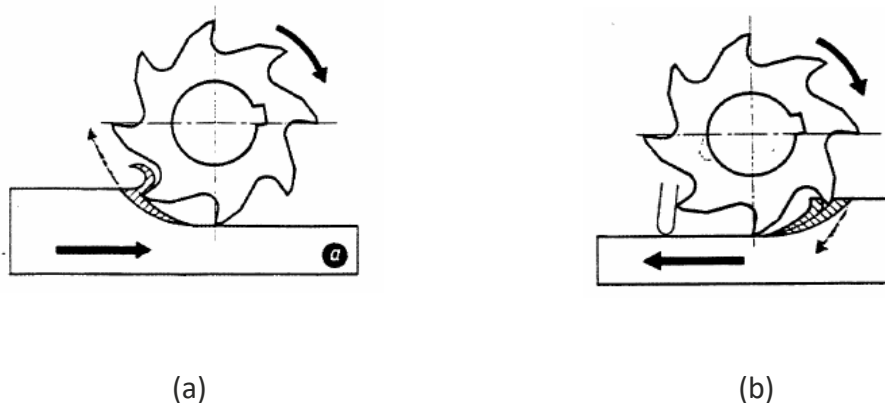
Fresagem com movimento a) discordante, b) concordante (adaptado de Gerling, 1977)
